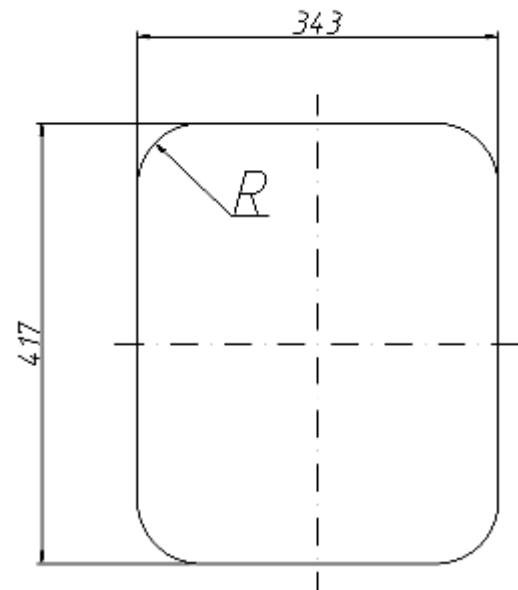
Коробчатая деталь типа «Крышка» и заготовка со скругленными углами
